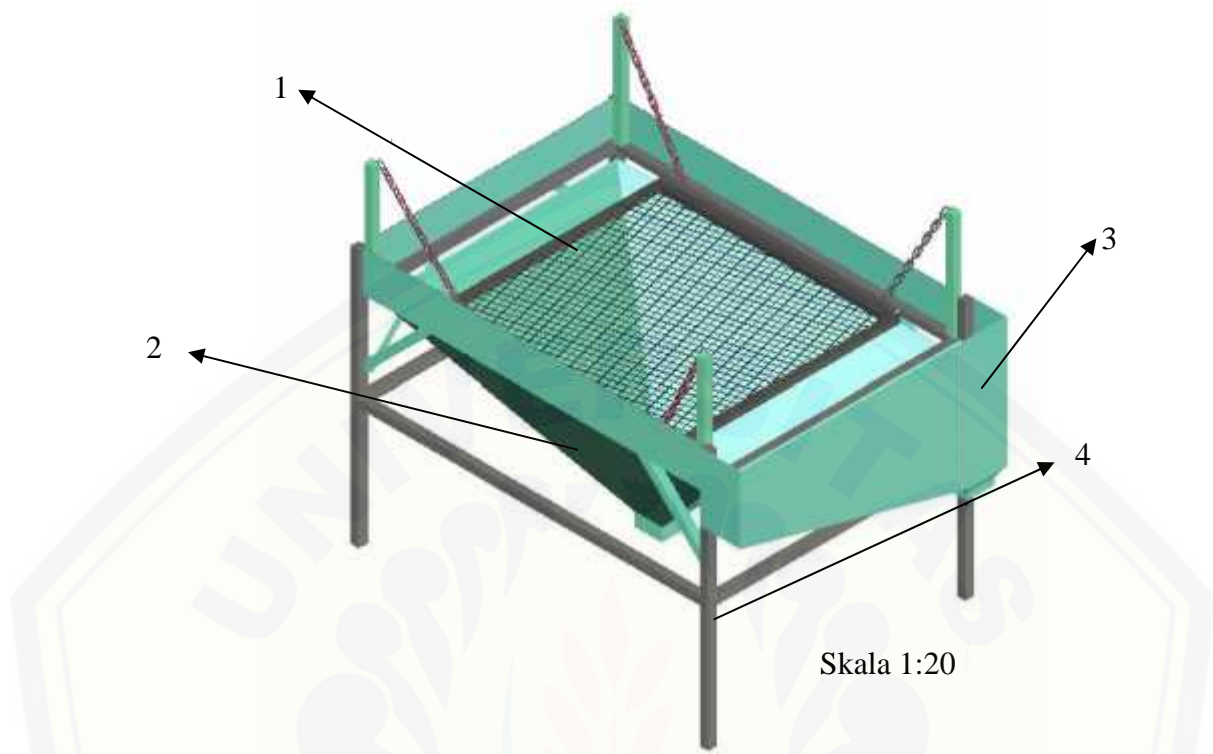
Ilustrasi Alat Pengayak Benih Dilengkapi dengan 3 Dimensi
